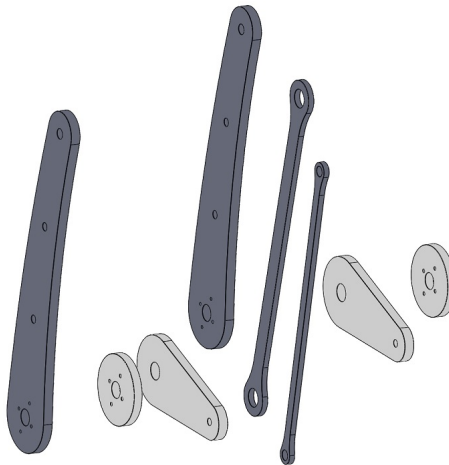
Vista explosionada del primer eslabón del robot manipulador.
